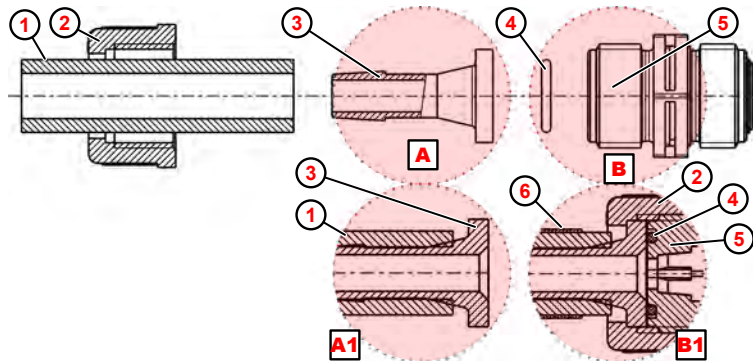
Collegamento tubi rigidi e tubi flessibili con raccordo filettato di fissaggio e fascetta tubo flessibile
